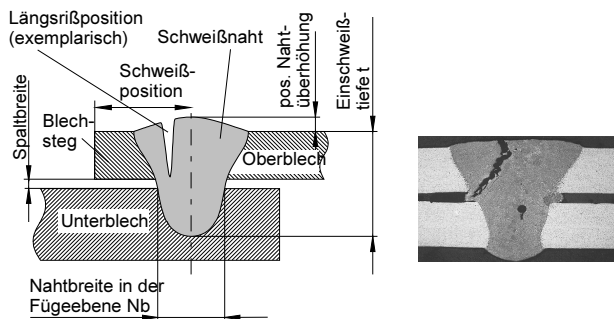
Rißproblematik beim Schweißen in Blechrandlage.
